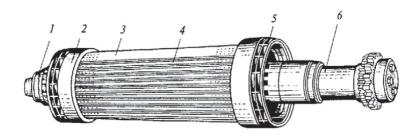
Внешний вид неявнополюсного ротора:
